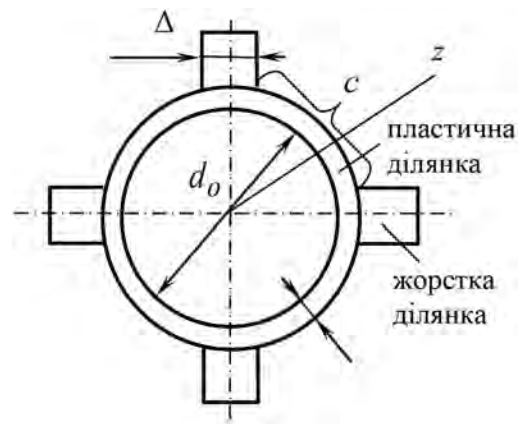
Заготовка з жорсткими та пластичними ділянками
